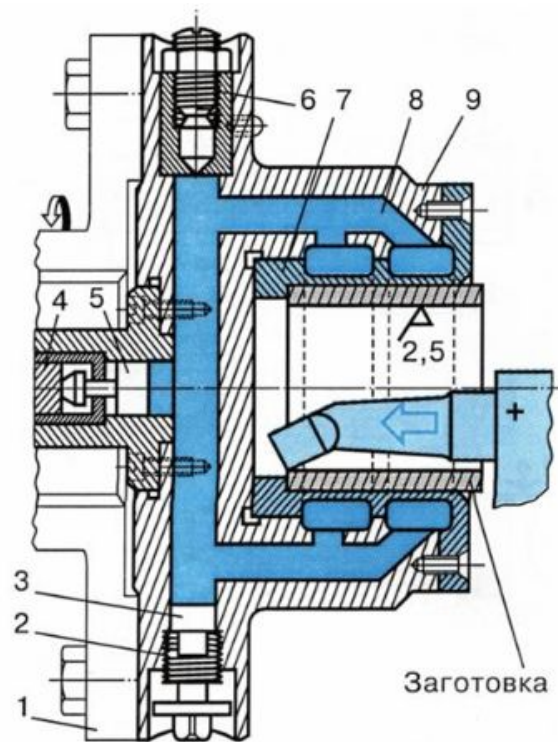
Застосування гідропластного патрону для закріплення тонкостінної втулки (гільзи): 1 – планшайба; 2- гвинт; 3,5 – плунжери; 4 – таяга від пневмоциліндра; 6- пробка; 7 – затискна втулка; 8 – гідро пласт; 9 - корпус
